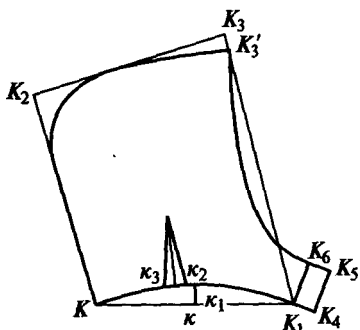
Чертеж конструкции втачного капюшона типа «шлем»
